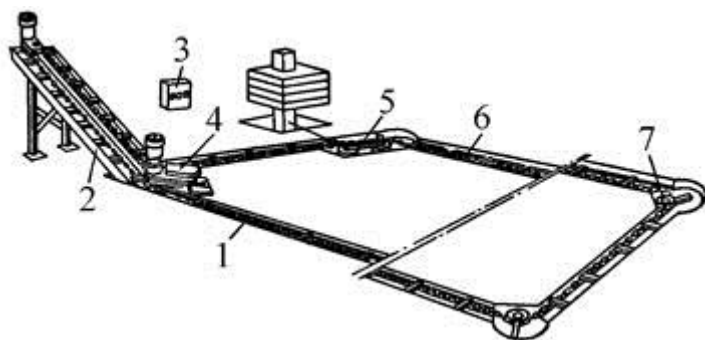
Транспортёр скребковый навозоуборочный ТСН-160:
